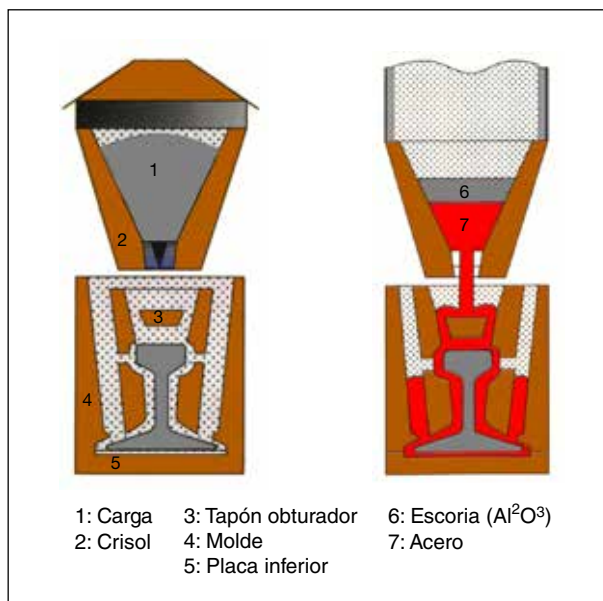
Esquema del proceso de soldadura aluminotérmica
